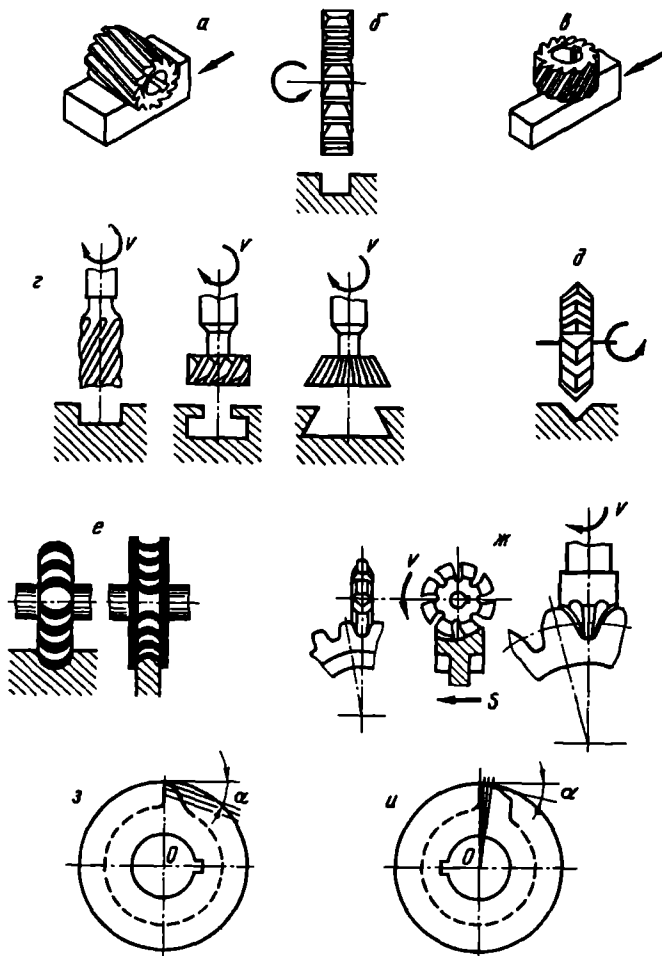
Типы фрез и операций, выполняемых фрезерованием
